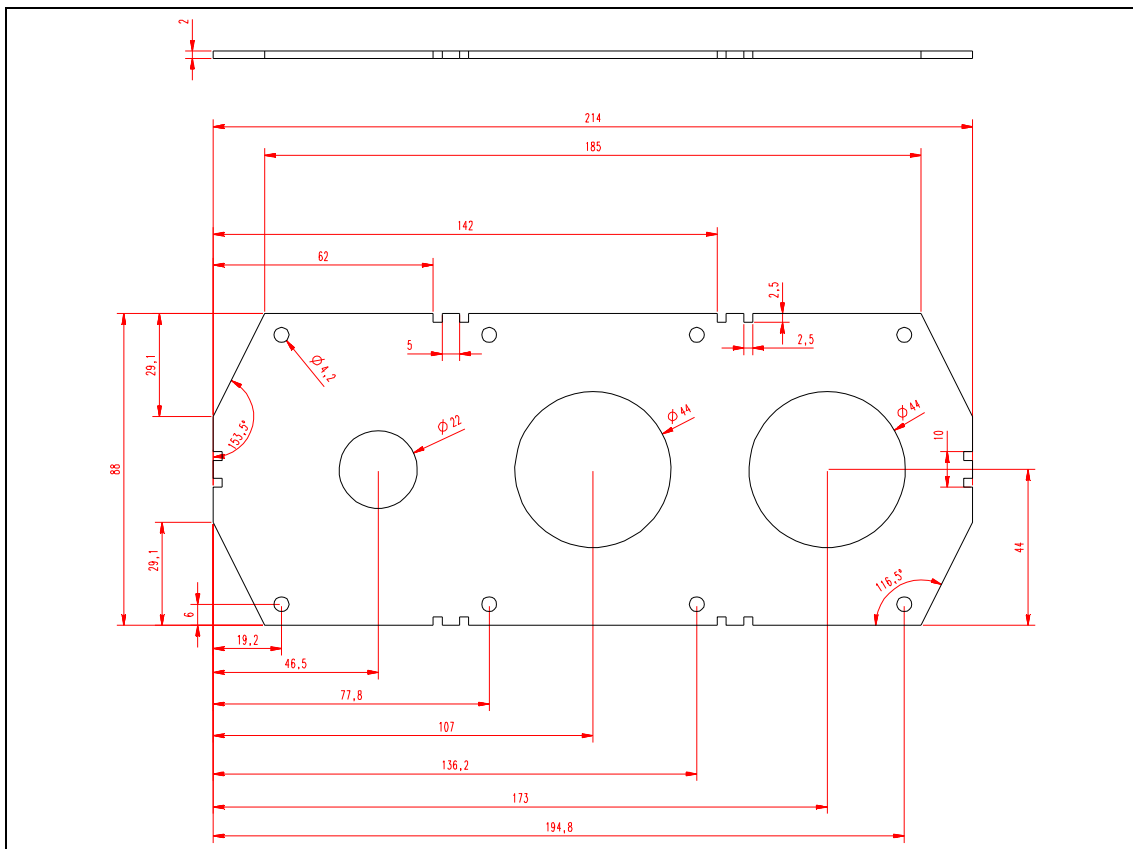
Plaque d'entrée des câbles, installation UL MM6
